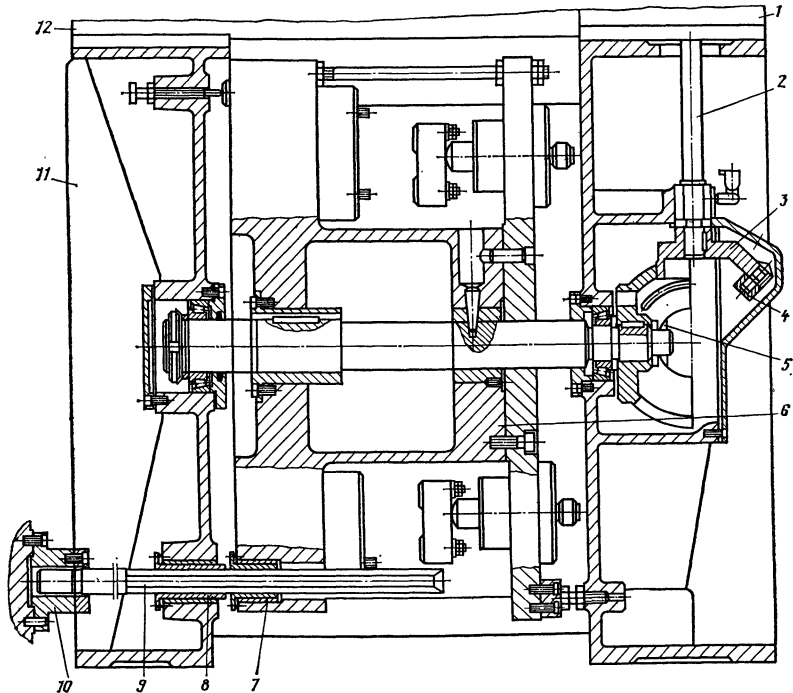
Компонка барабанного приспособления с мальтийским приводом поворота
